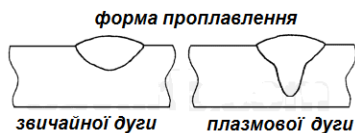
Типові форми перерізу шва для різних способів зварювання
